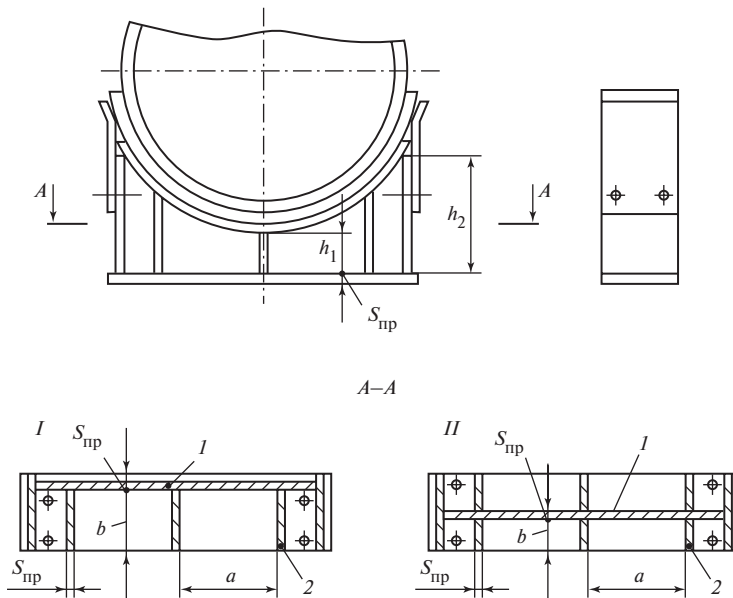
Седловая опора и ее конструктивные элементы:
